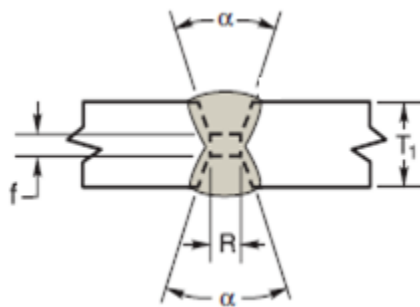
Sección de la soldadura DSW con tacón central (Fuente: www.monografias.com)
